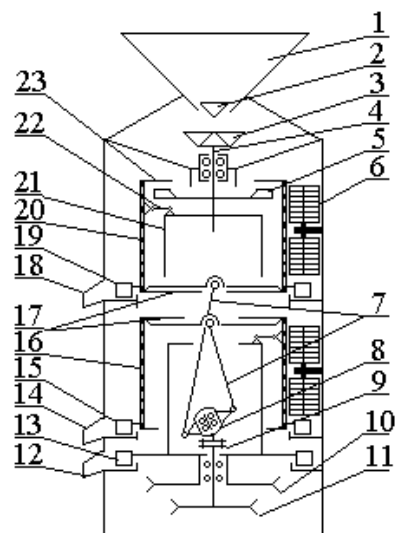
Конструктивная схема лабораторного виброцентробежного сепаратора: 1 – бункер; 2 – заслонка; 3 – разбрасыватель конический; 4 – вал; 5 – разбрасыватель дисковый; 6 – очиститель копирующий дисковый; 7 – шатуны; 8 – вибровозбудитель; 9 – соединение фланцевое; 10, 11 – шкивы; 12, 14, 18 – лотки; 16 – решето сортировальное; 17 – траверсы; 13, 15, 19 – скребки; 20 – решето подсевное; 21 – ротор; 22 – подвески; 23 – барабаны цилиндрические
